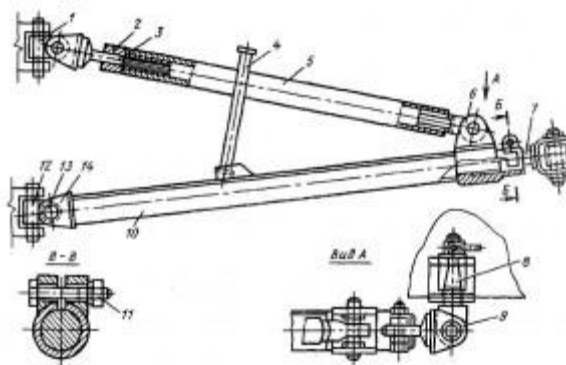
Толкатель бульдозера: 1, 12 и 14 — крестовины для присоединения раскосов и толкателей к отвалу; 2 — разъемные вкладыши; 3 — винтовая нарезка раскосов; 4 — рукоять с винтовой нарезкой для изменения длины раскосов; 5 — раскосы; 6 — проушины; 7 — винтовая нарезка для изменения длины толкателей при повороте отвала; 8 — шкворень; 9 — вилка; 10 — толкающее устройство; 11 — узел крепления; 13 — пальцы
